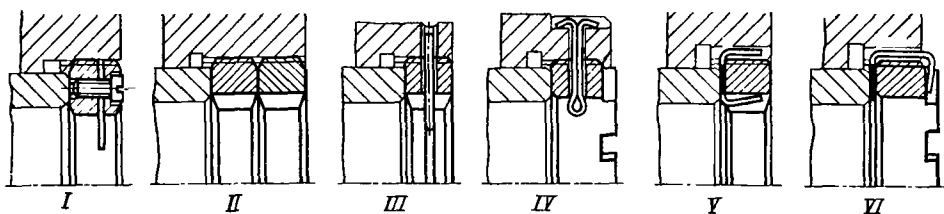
Способы стопорения внутренних кольцевых гаек:
